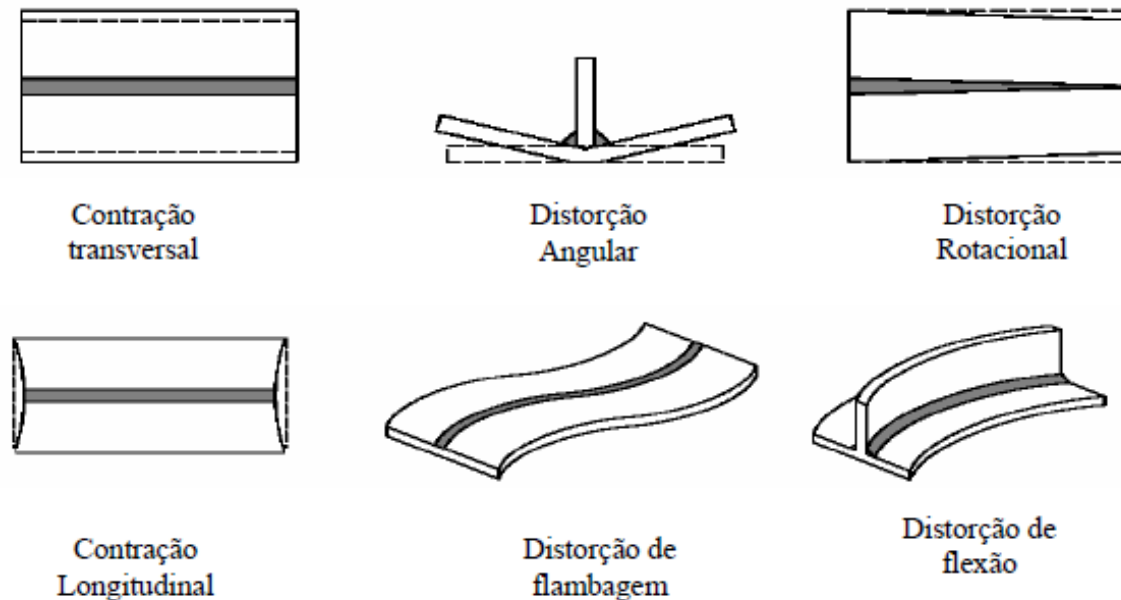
Tipos de imperfeições geométricas de fabricação [24]
